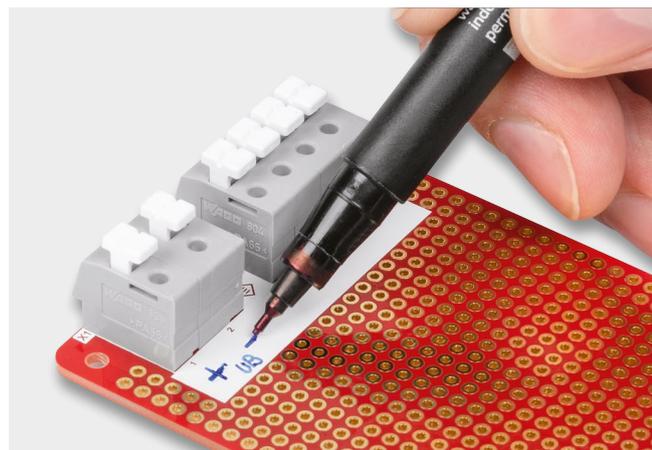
Die weißen Felder auf der Platine können beschriftet werden.
